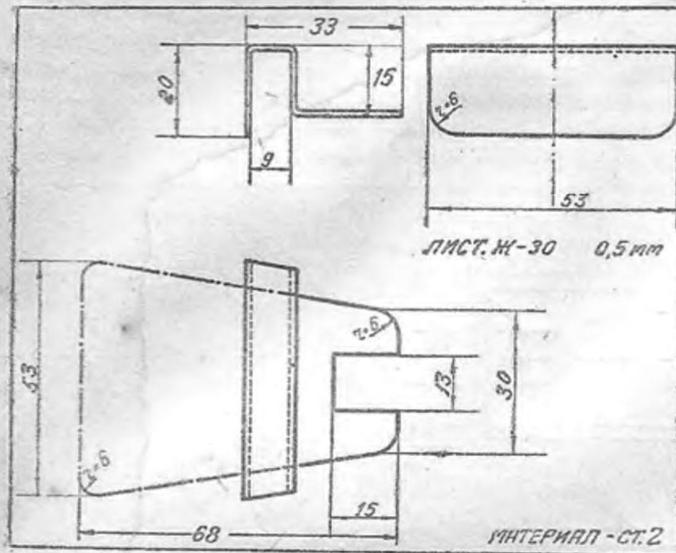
Пружина неподвижной стойки автомата для смены пластинок
